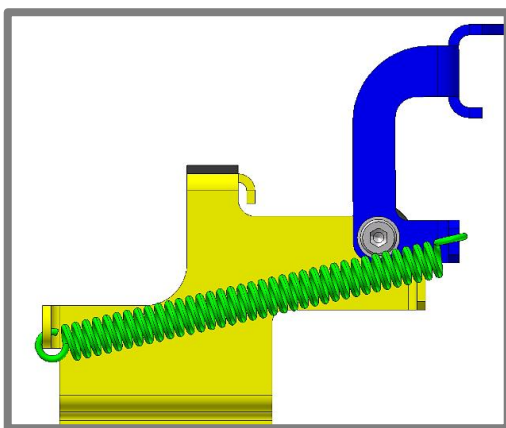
Pomocný přídržný mechanismus – uzavřený stav (modrá – horní profil, žlutá – spodní profil, zelená pružina)
